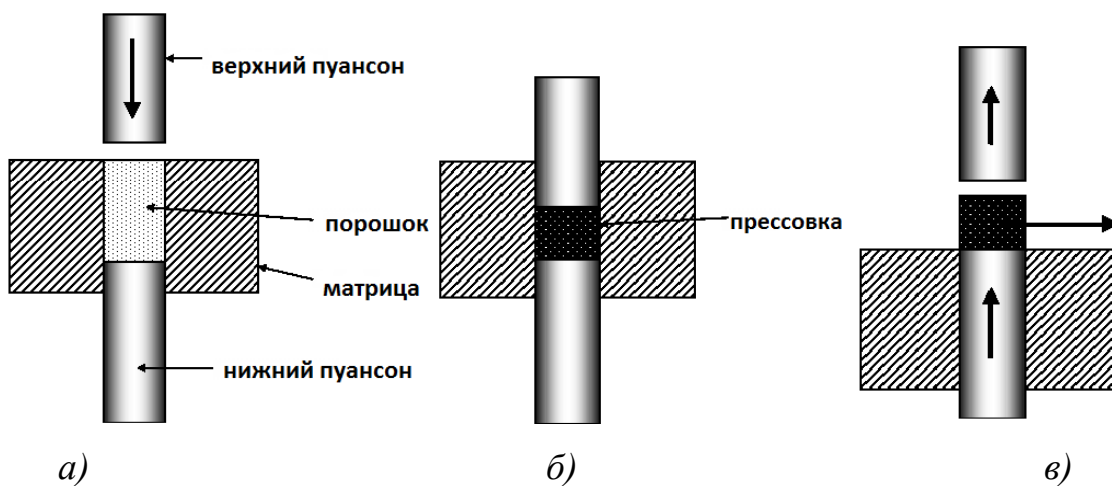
Стадии холодного прессования: а) засыпка порошка, б) прессование, в) выпрессовка
